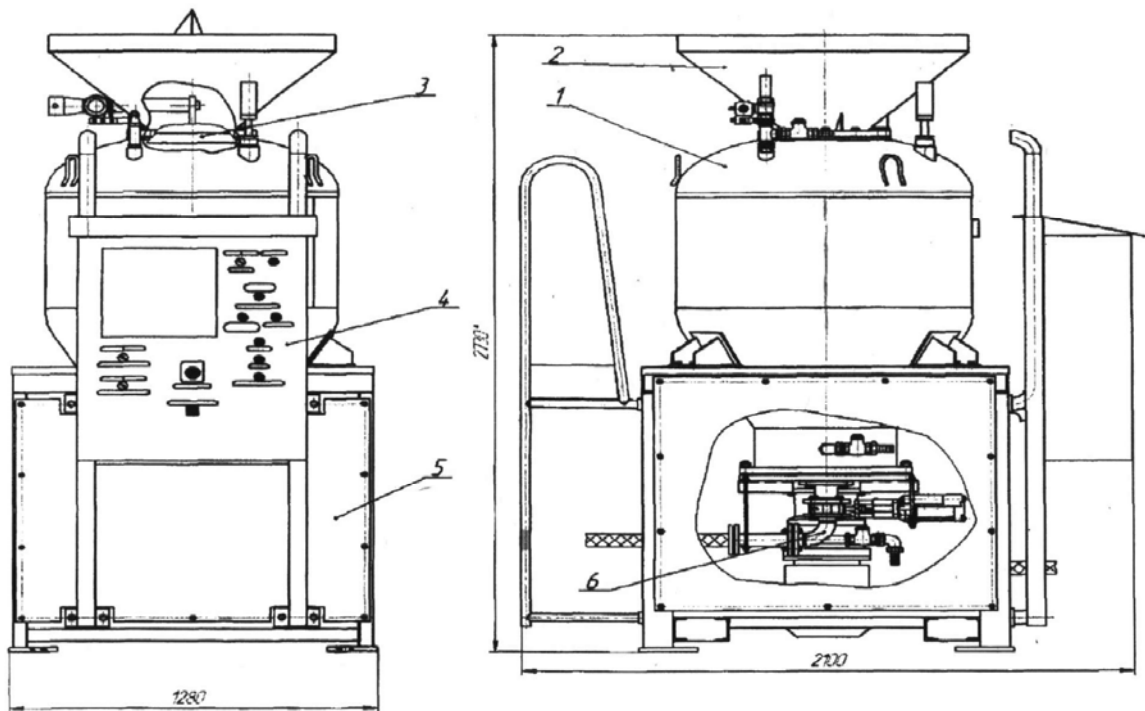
Конструкція пневмомеханічної торкрет-установки
